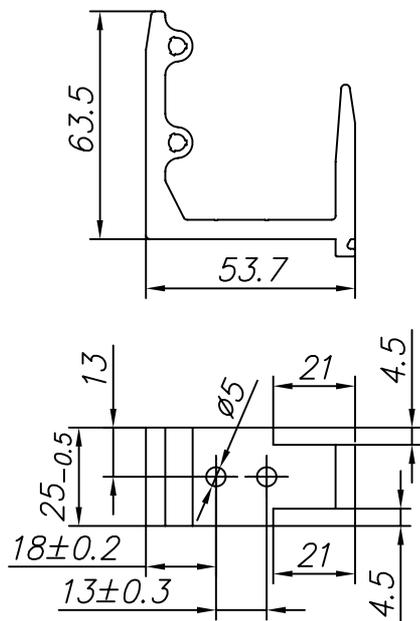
Изготовление соединителя FLGU.400.0913
